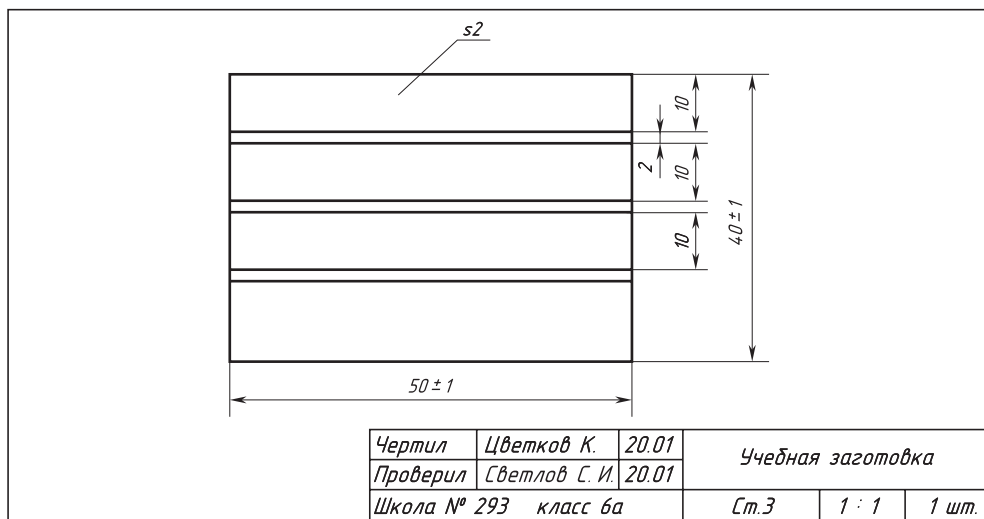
Чертёж учебной заготовки для рубки полос
